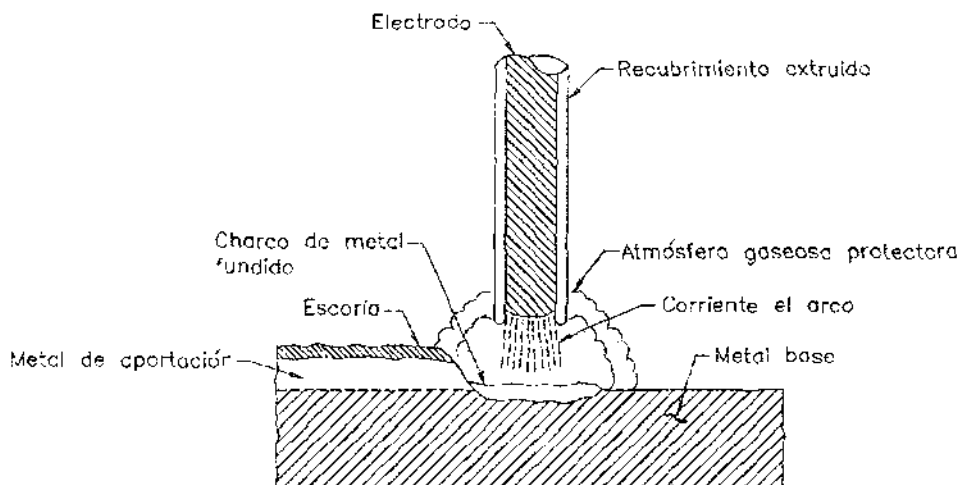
SOLDADURA DE ARCO, CON PROTECCION.
